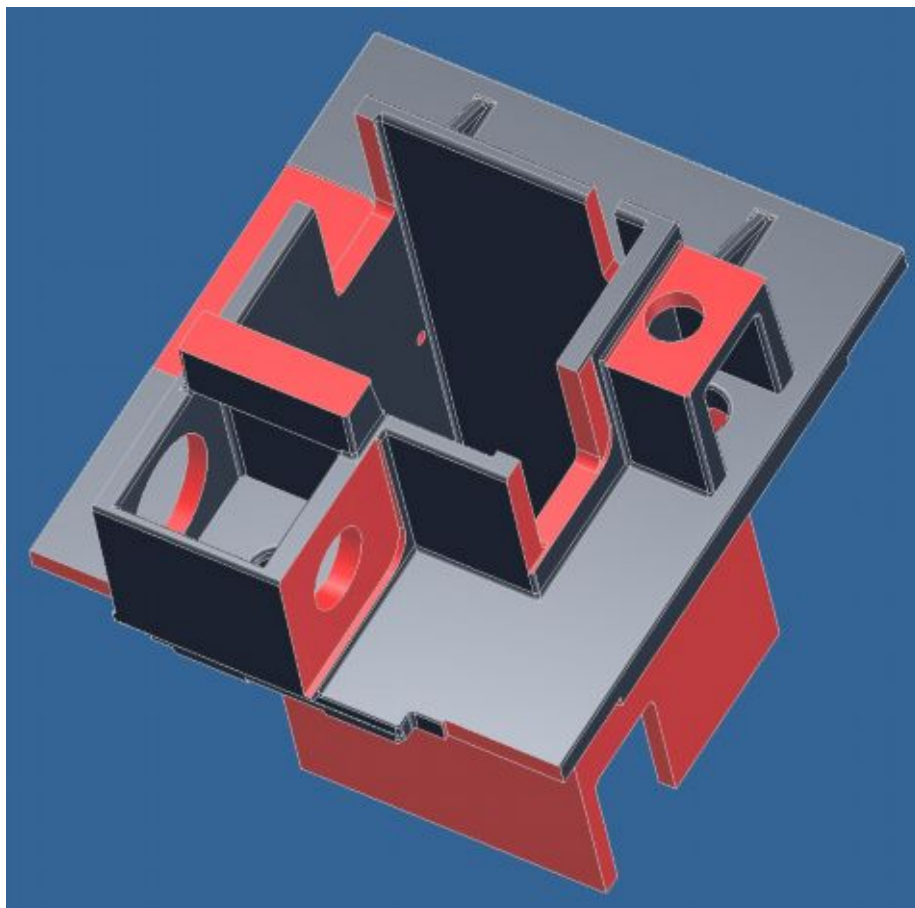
Vyhrubovaný odlitek po upnutí č.3
